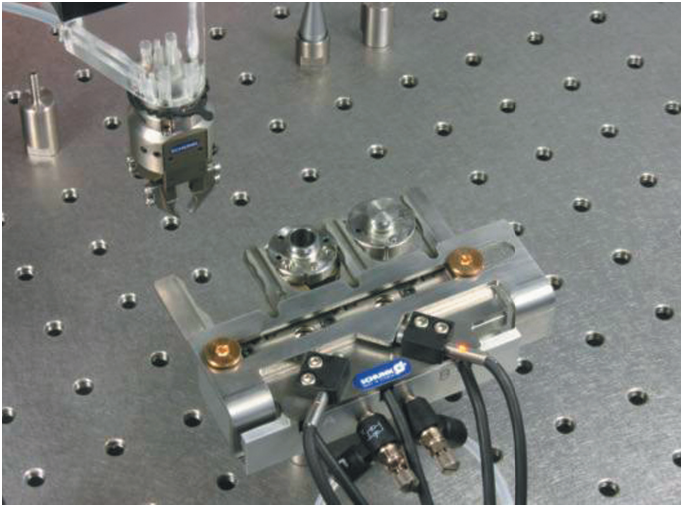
Встроенный робот для перемещения заготовок пластин и обработанных микродеталей
